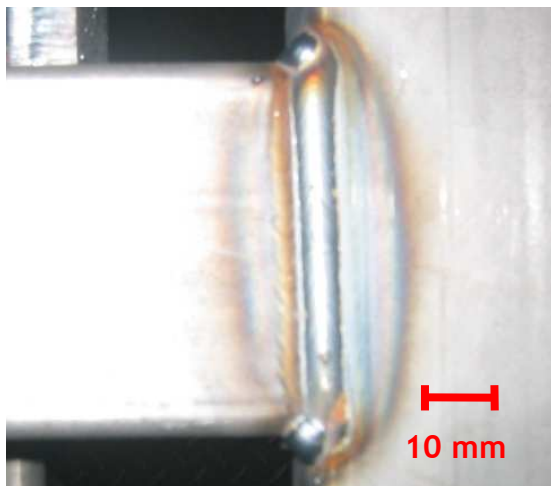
IMAGEM REPRESENTATIVA DOS CORDÕES DE SOLDADURA EFECTUADOS COM O PROGRAMA B
